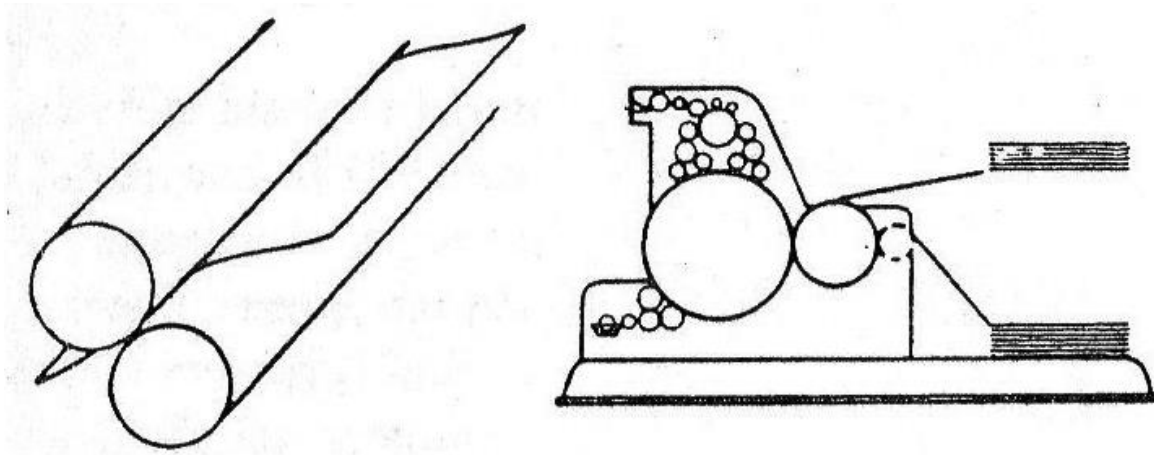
Máquina de impresión directa rotativa (der.) y su principio de impresión (izq.).
